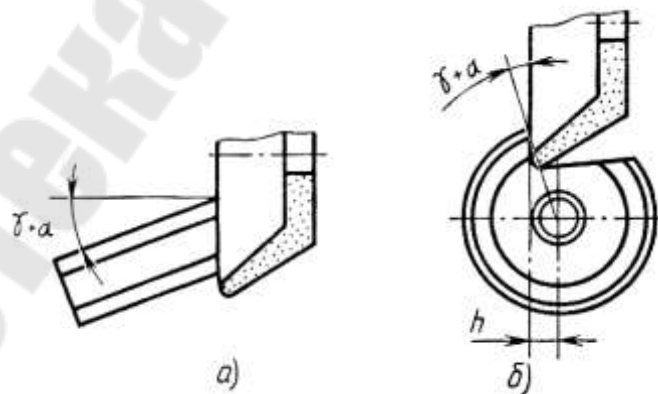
Схемы заточки фасонных резцов по передней поверхности: а – призматического; б – круглого
